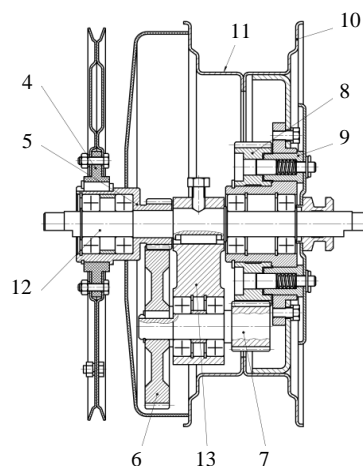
Осевое сечение барабана лебедки со встроенной в его конструкцию двухступенчатой зубчатой передачей:
